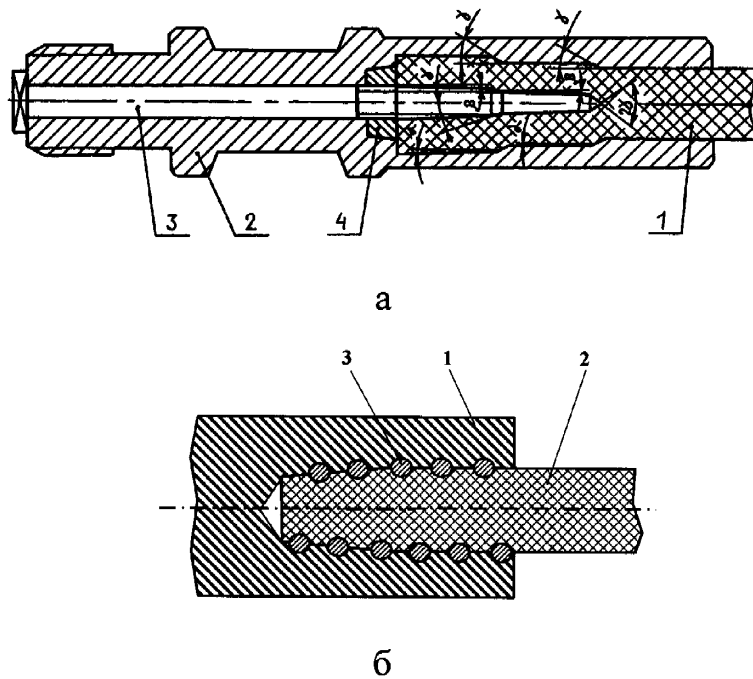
Конструкції клинового роз'ємного з'єднання (а)
